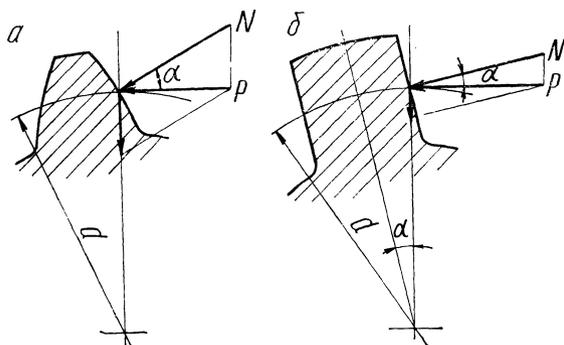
Схема действия сил на боковой поверхности шлицев для эвольвентного (а) и прямобоочного профиля (б).
